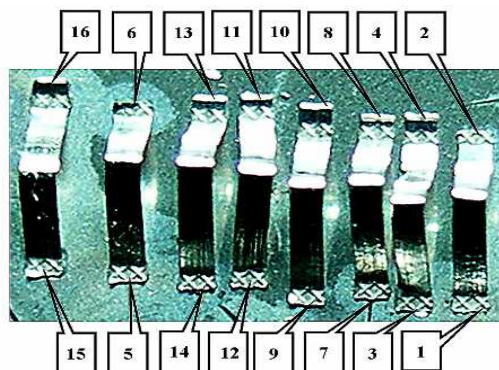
Внешний вид контролируемых соединений ленточными перемычками
